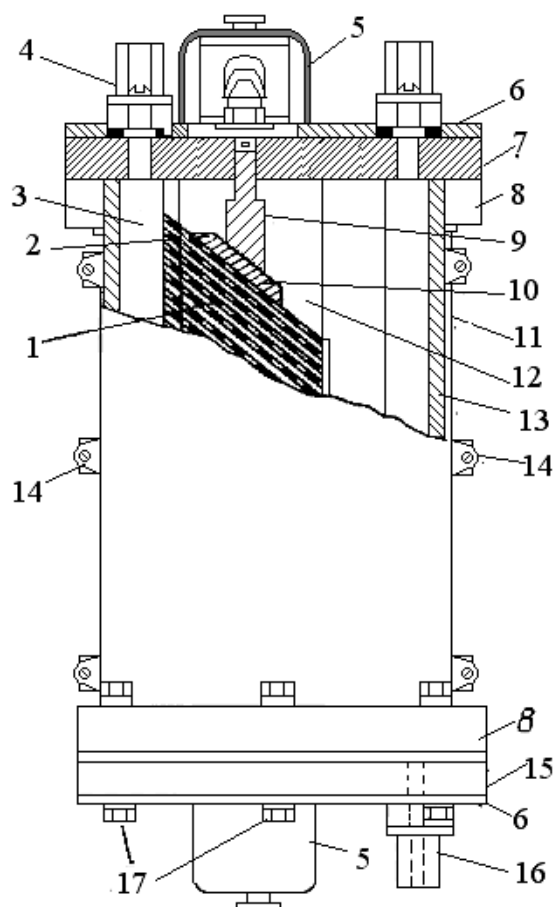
Біполярний електролізер для одержання гіпохлориту натрію: 1 — електроди; 2 — пази; 3 — стійки; 4 — штуцер для відводу розчину гіпохлориту; 5 — коробки; 6 — стяжні пластини; 7 — кришка; 8 — фланці; 9 — струмовідводна штанга; 10 — рухлива шайба; 11 — кожух; 12 — скошені блоки; 13 — корпус; 14, 17 — болти; 15 — днище; 16 — штуцери для введення живильного розчину
